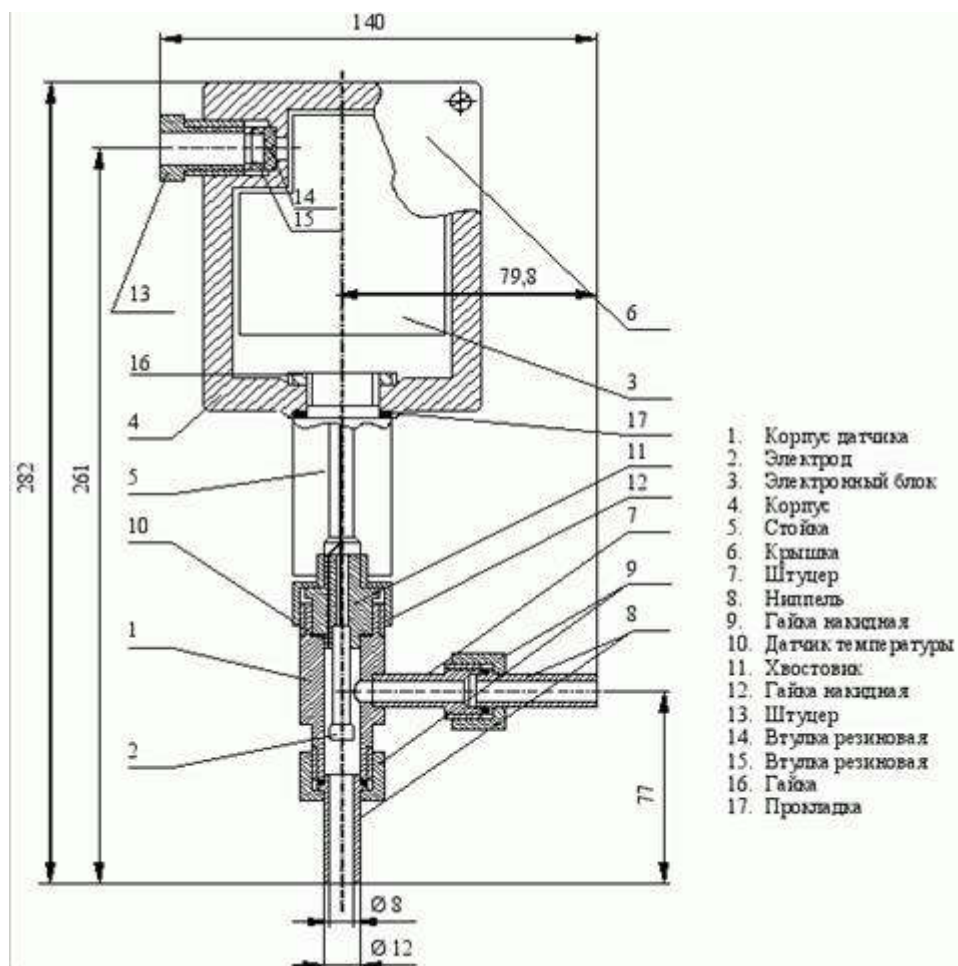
Первичный преобразователь с корпусом из дюралюминия, тип «Д», проточный, с штуцерами
